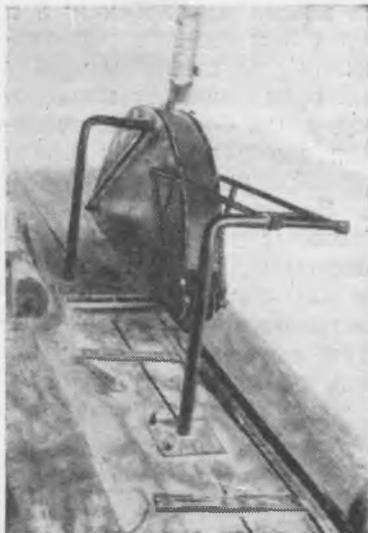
Общий вид безопасного колпака и его крепления к столу станка.
